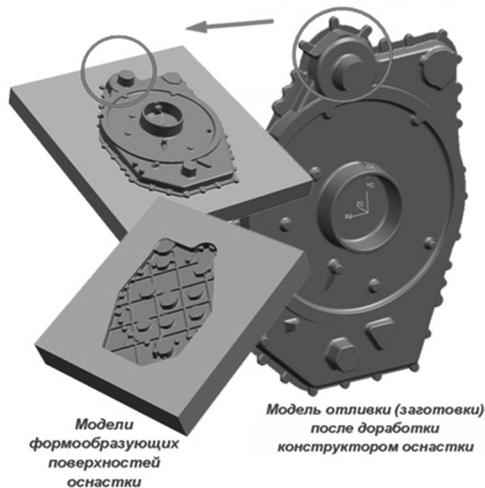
Автоматическое отображение изменений в модели отливки и формообразующих поверхностях
